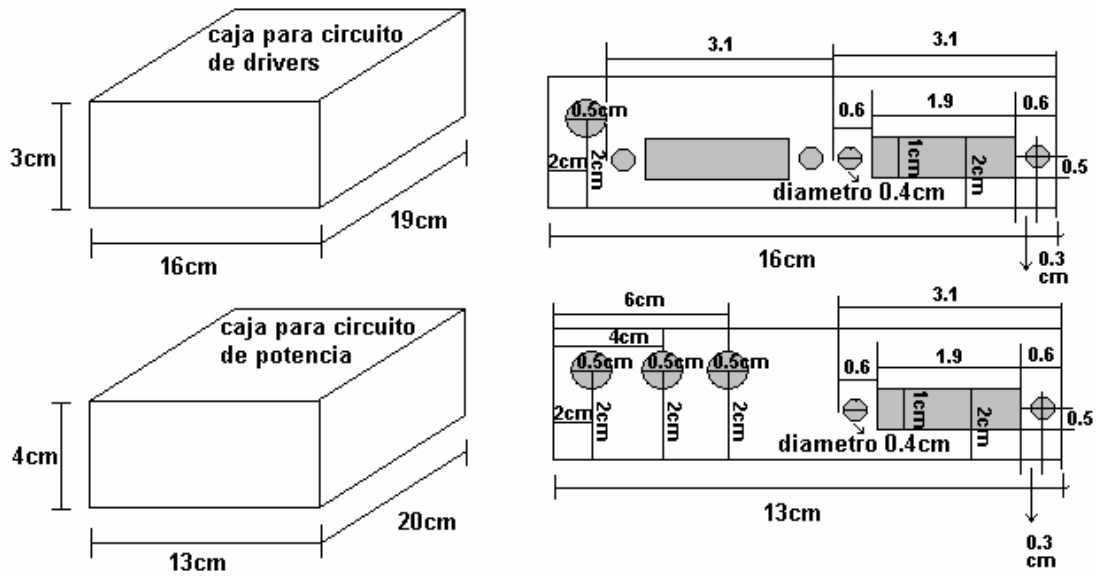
16 Diseño y dimensiones de las cajas para las placas impresas.
